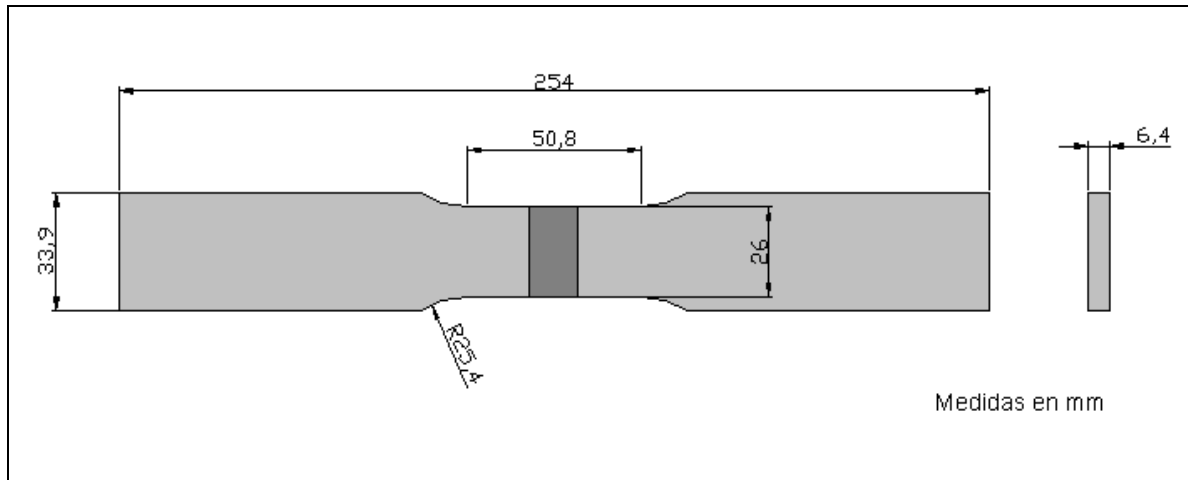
Dimensiones de la probeta de Tracción en juntas soldadas según AWS B4.0-98.
